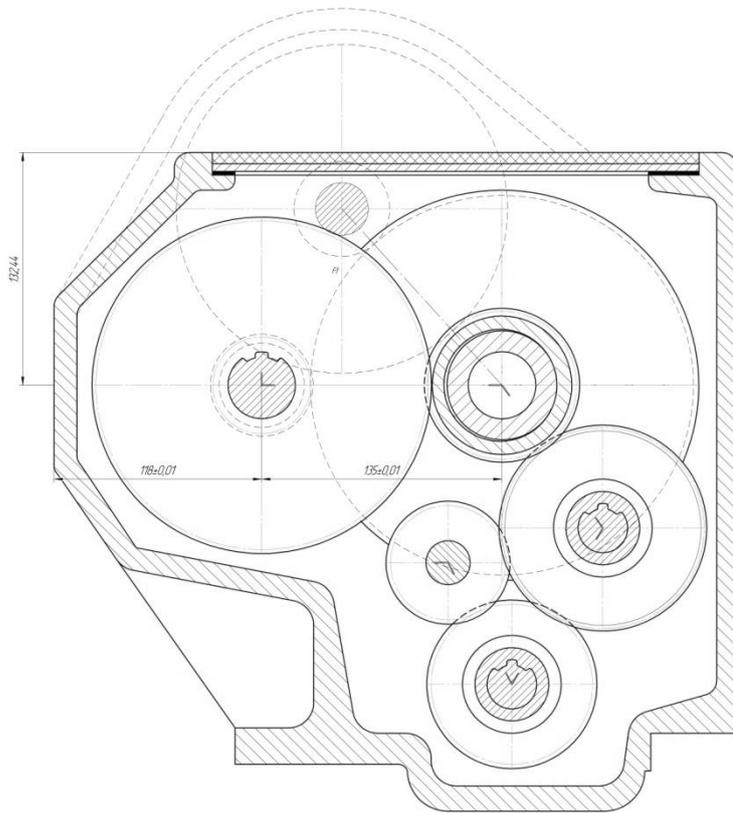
Базовая компоновка привода главного движения станка модели ИТ-1
